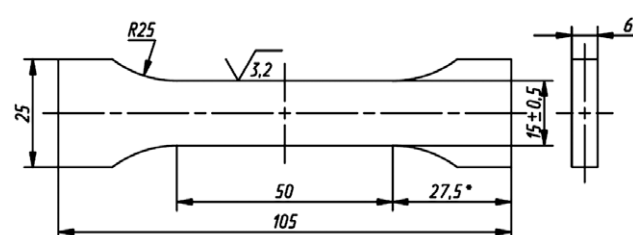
Образец для испытания на растяжение: напечатанный алюминий AMg5 и листовой AMg5.
